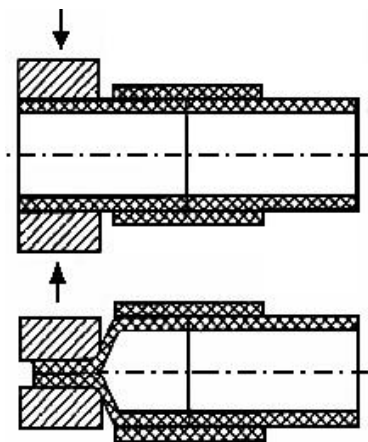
Схема испытаний образцов – сегментов на сплющивание
